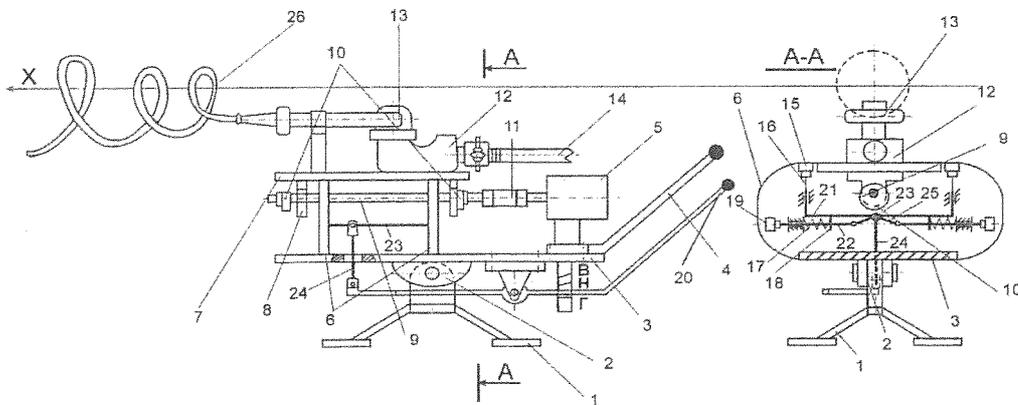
Конструктивно-кінематична схема лафетного вібраційного ствола: 1 - опорна основа; 2 - шарнірне з'єднання; 3 - нерухома основа вібраційного стола; 4 - ручка керування; 5 - привід обертового руху; 6 - ресорна підвіска рухомої частини вібраційного стола; 7 верхня частина стола, яка вібрує; 8 - підшипникові опори валу дисбалансів; 9 - вал дисбалансів; 10 - дисбаланси; 11 - еластична муфта; 12 - приймальний корпус; 13 - ствол; 14 - напірний патрубок; 15 - притисна подушка (вертикальна); 16 - гнучка пластина; 17 - пружина; 18 - упорна шайба; 19 - притисна подушка (горизонтальна); 20 - ручка - перемикач; 21 - коромисло; 22 - шток; 23 - вісь приводу тяги; 24 - вертикальна тяга; 25 - штовхач; 26 - коловогвинтовий або еліпсогвинтовий компактний струмінь рідини.
